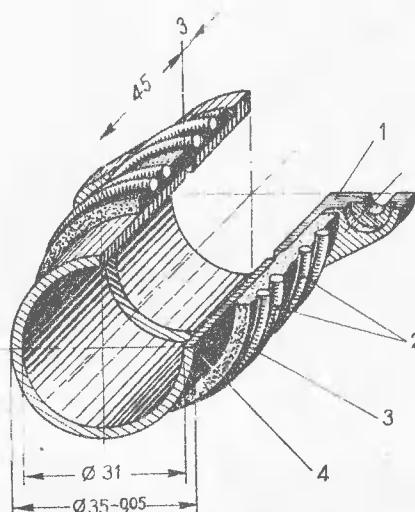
Патрубок, смягчающий вибрацию карбюратора: 1 — стандартный патрубок крепления карбюратора; 2 — хомуты (или проволока); 3 — дюритовый шланг; 4 — втулка (самодельная).
